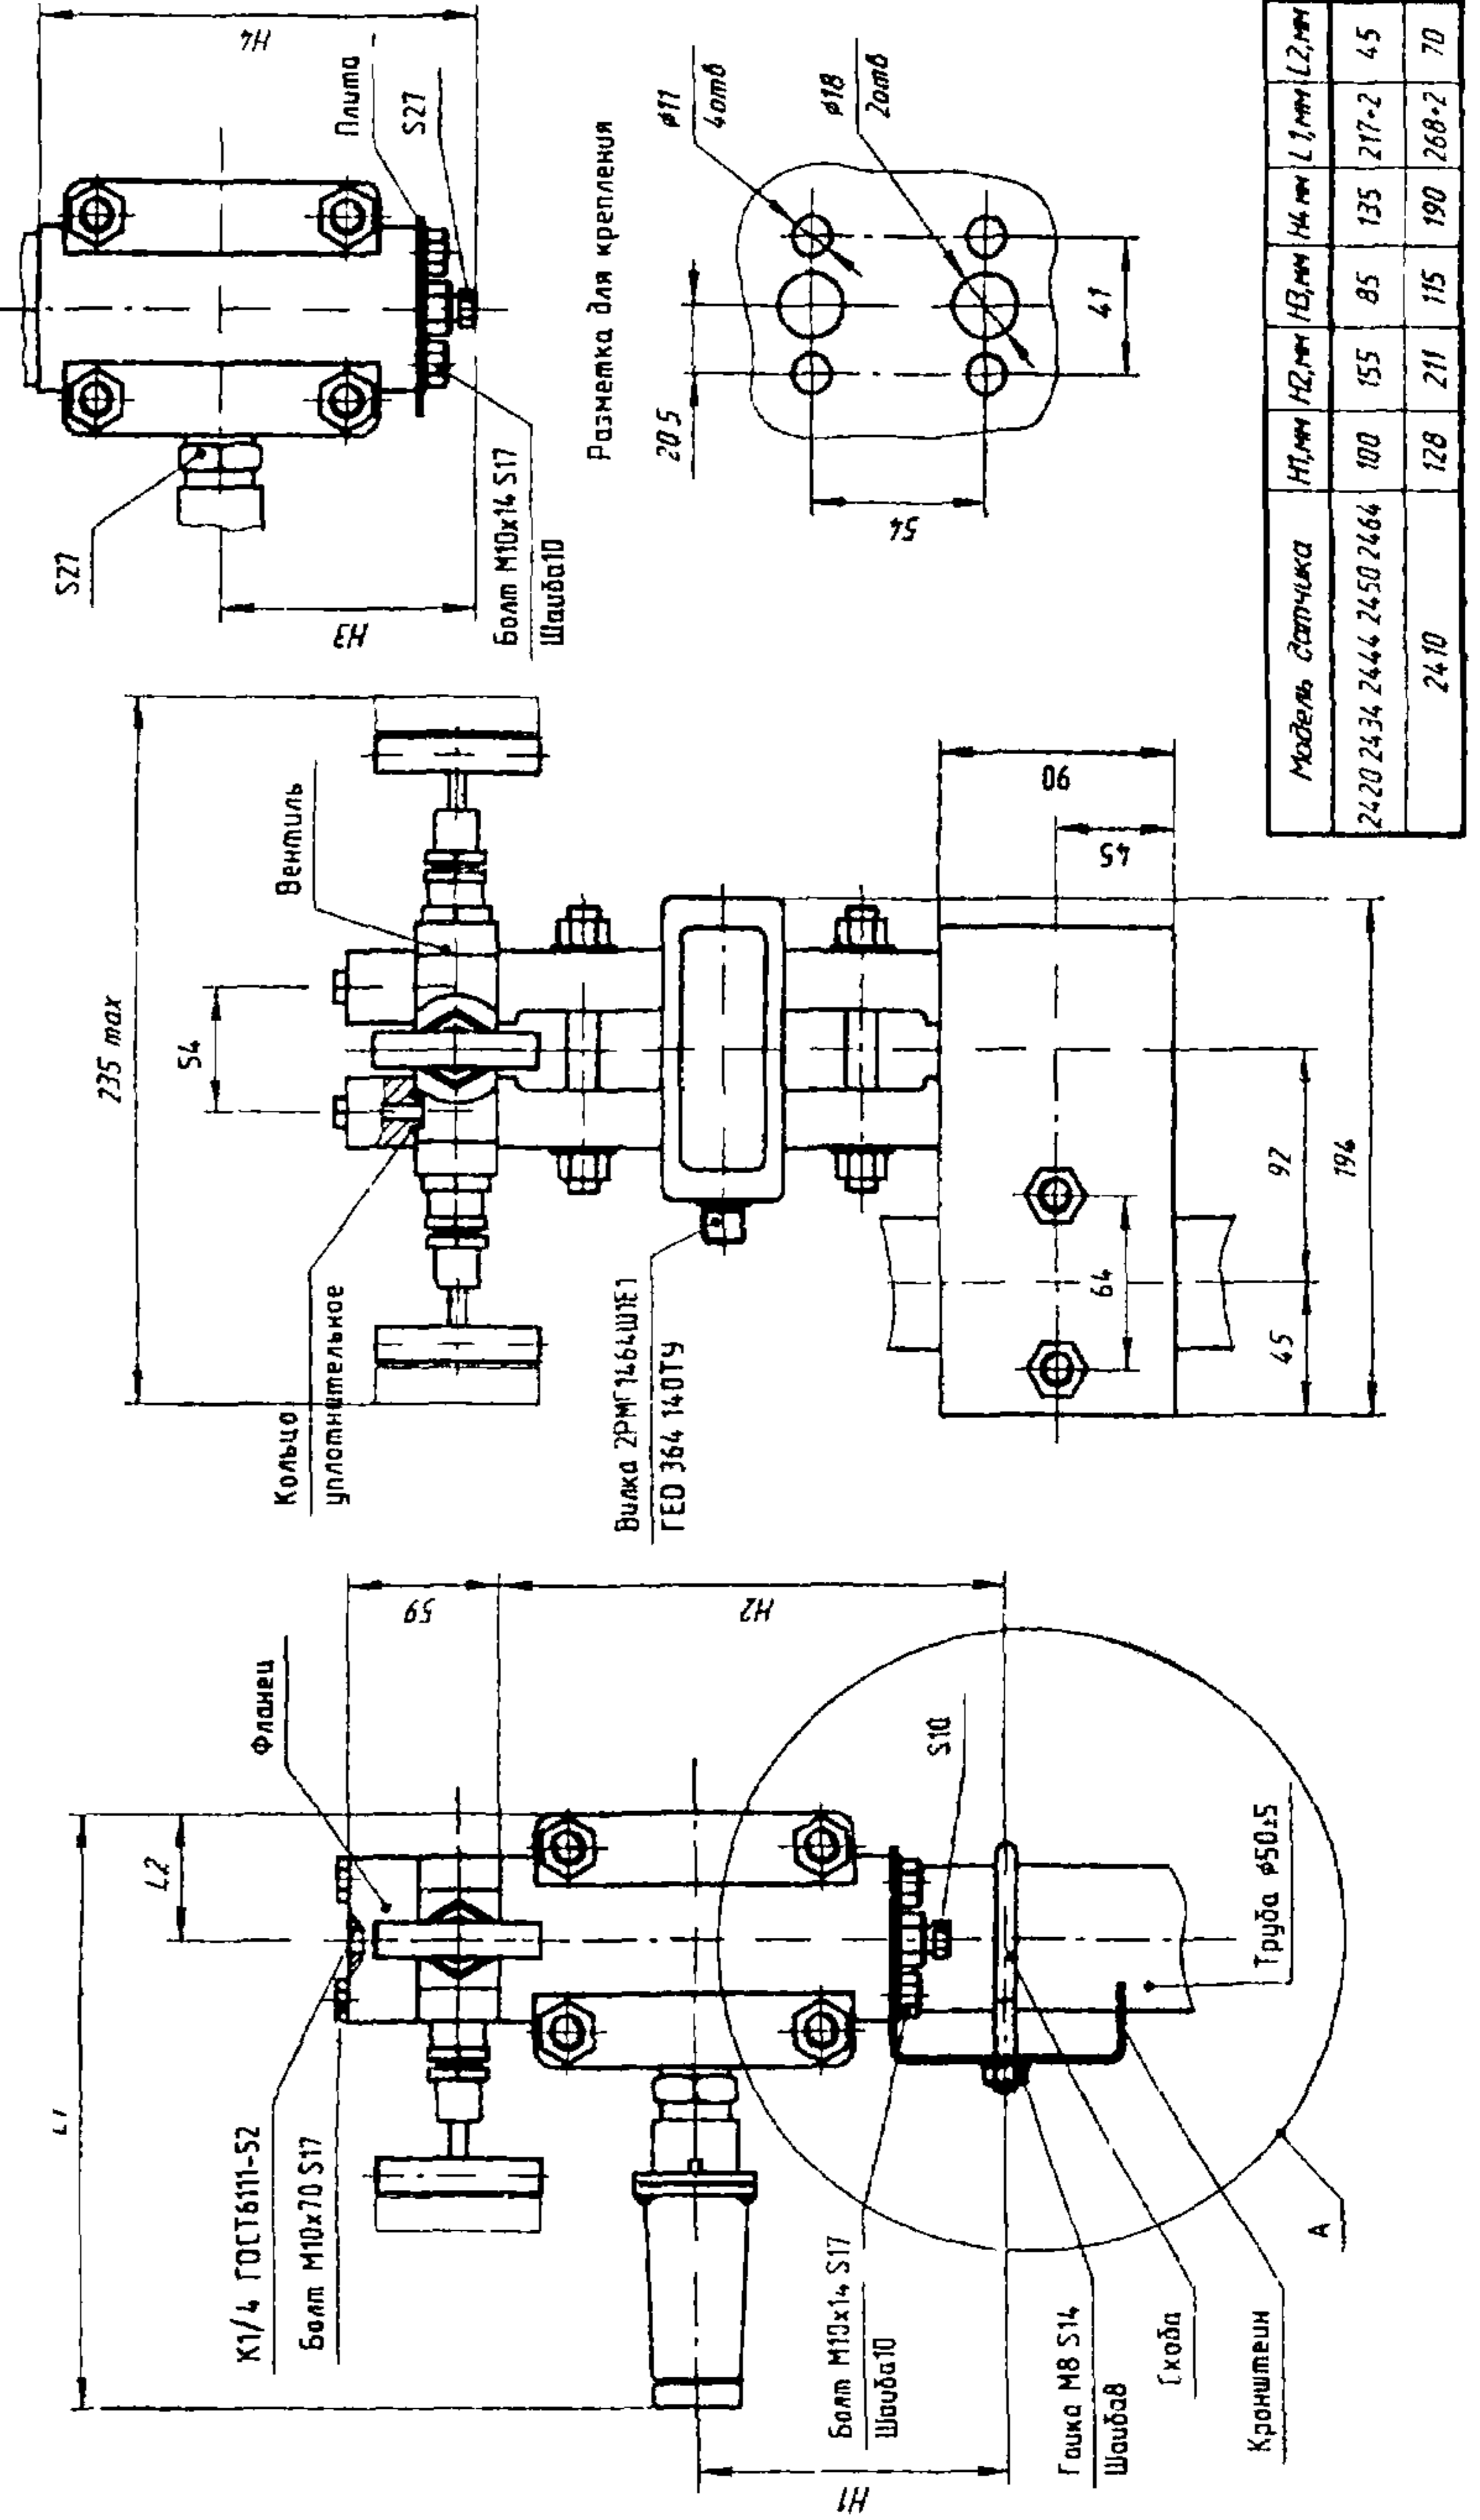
Установочные и присоединительные размеры датчиков модели 2410, 2420, 2434, 2444, 2450, 2464 с установленным трехвентильным блоком фланцами
